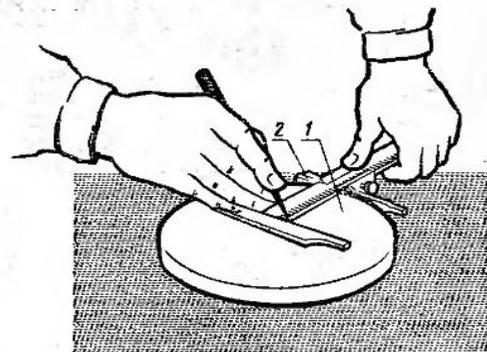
Разметка заготовки штангенциркулем с широким упором:
